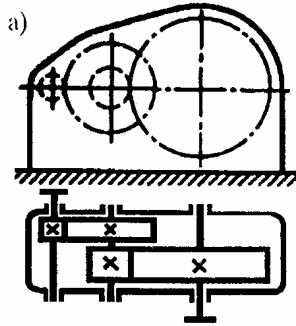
Кинематические схемы цилиндрических двухступенчатых редукторов (Ц2)
